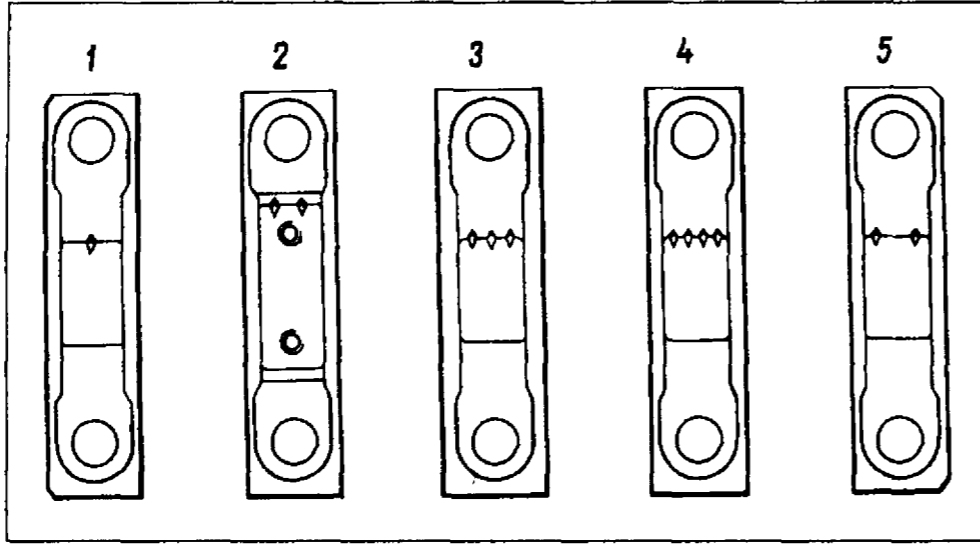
Метки на крышках коренных подшипников. Счет крышек ведется от стороны привода распределительного вала
